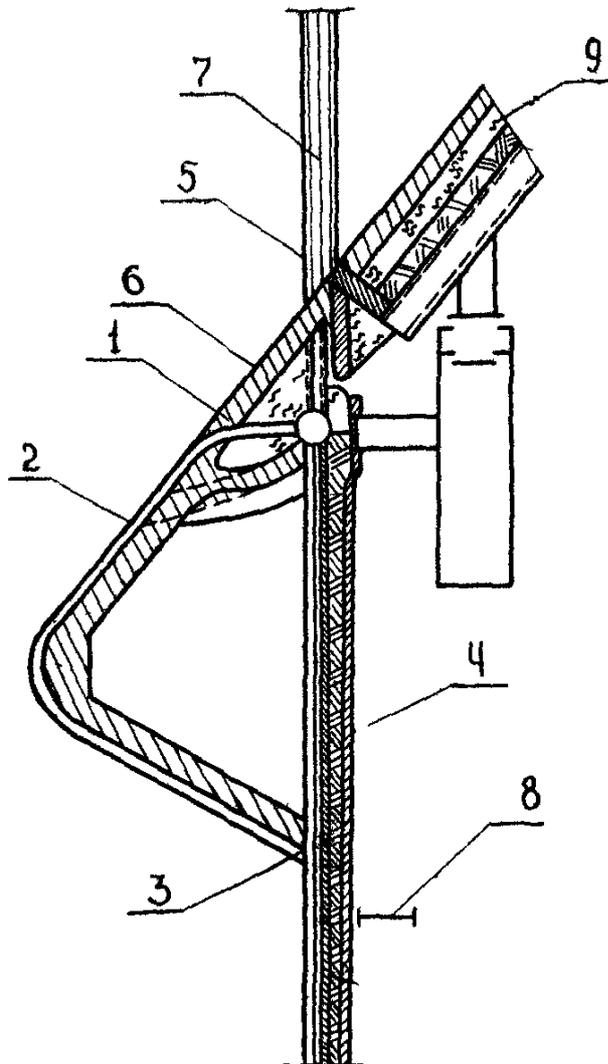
Конструкция выступа в глубину топочной камеры (зуб пережима)
